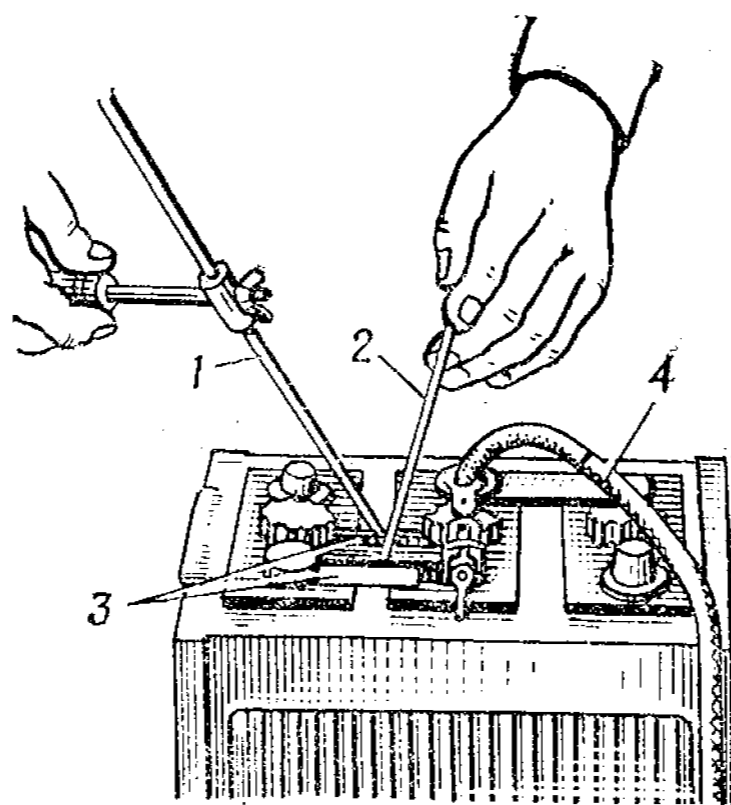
Сварка межаккумуляторного соединения встык:
